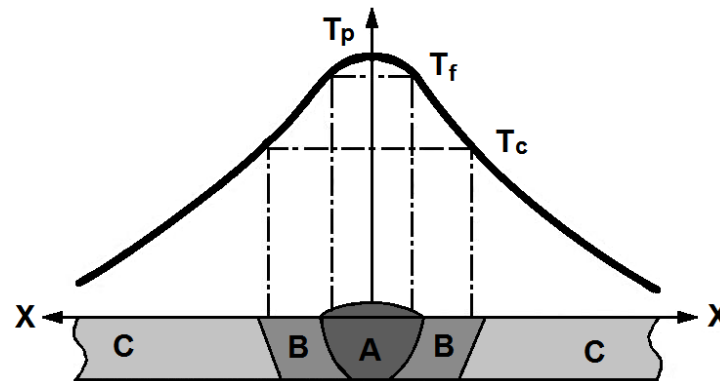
Ciclo térmico durante la soldadura (18, 73)
